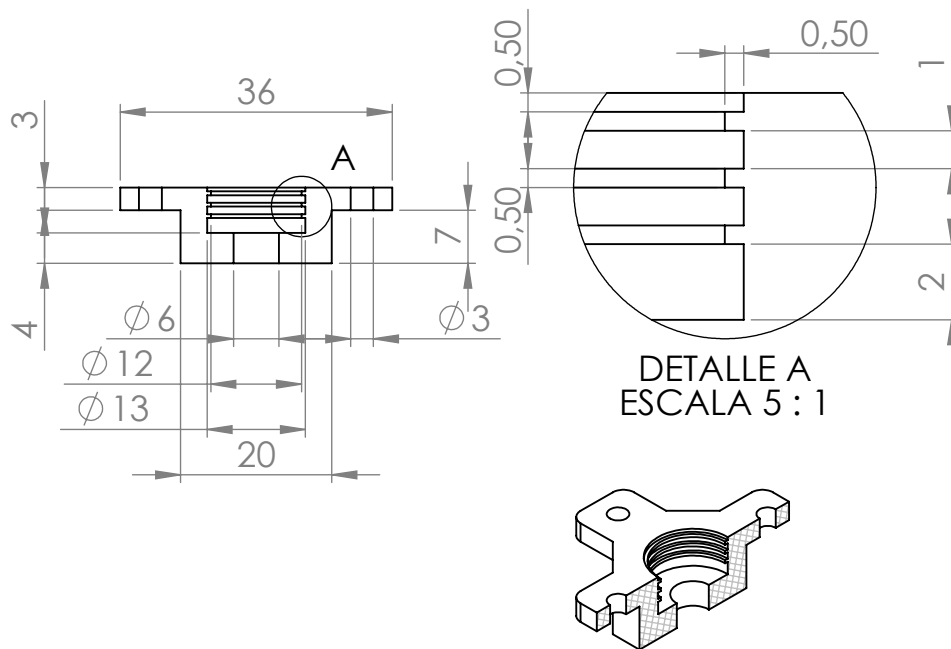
Vista en corte del molde del *Robot Shear* parte B
